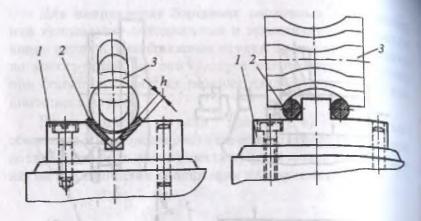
Специальные установы: 1 - установочный габарит; 2 - щупы для настройки инструментов; 3 - фреза
